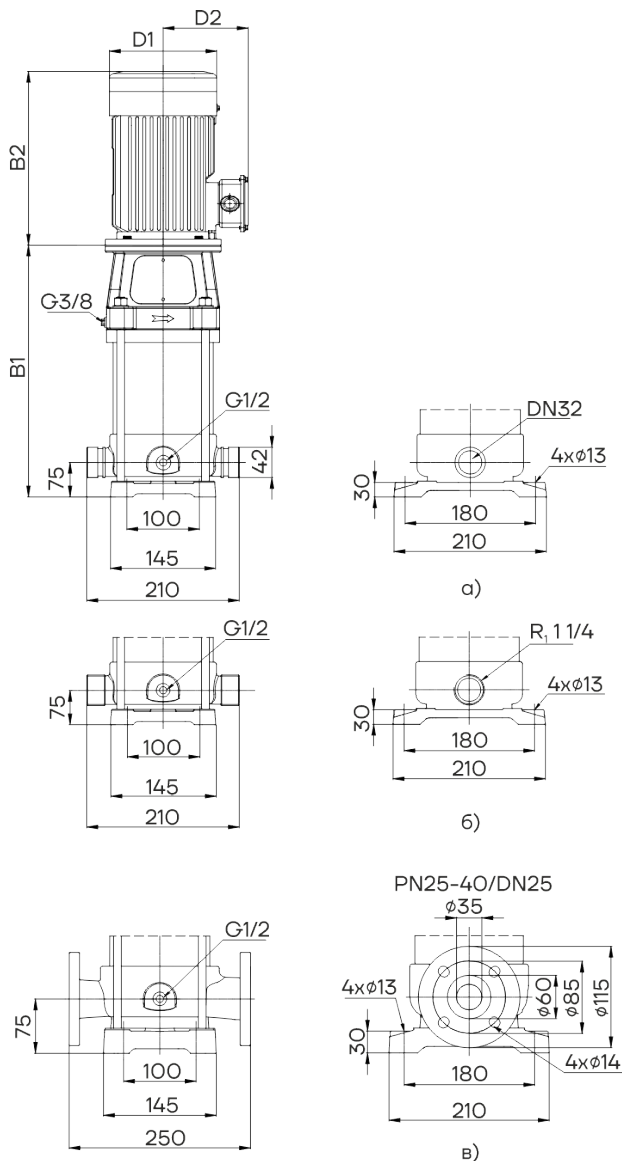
А Габаритно-присоединительные размеры VMB(F)-H 1, 2,
